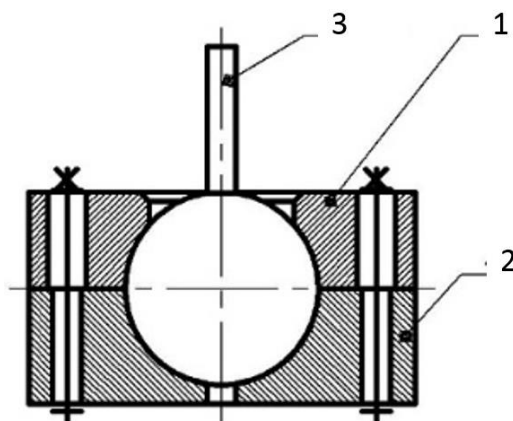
Шарнир шаровой 1 – Крышка, 2 – подпятник, 3 – палец шаровой
